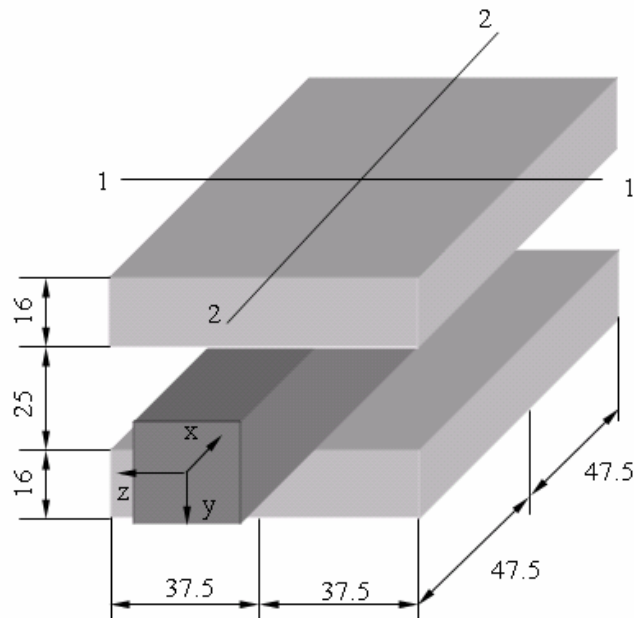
Detalle de la masa adosada a la viga (medidas en mm).
